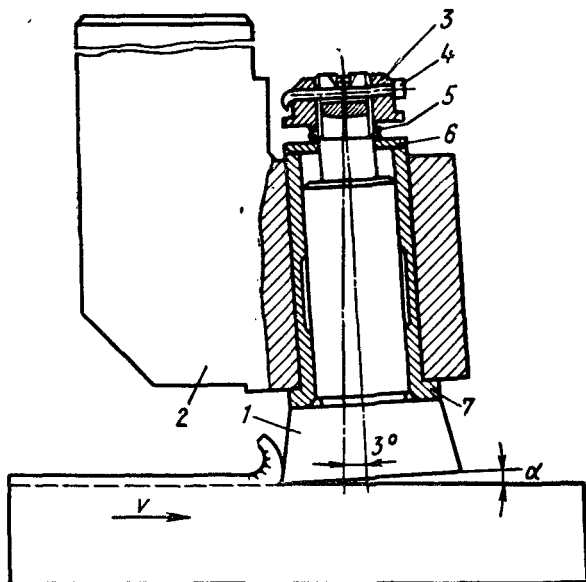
Чистовой строгальный вращающийся резец для обработки стали
